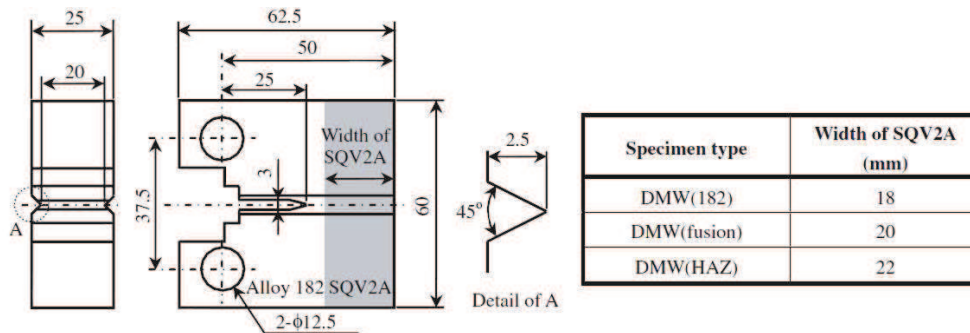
Forme et dimensions d'une éprouvette CT [OGA 12]
